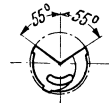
Tieflochbohrer mit eingedrücktem Ölloch und angeschweißtem Rohrschaft. 5...18 mm \varnothing .
